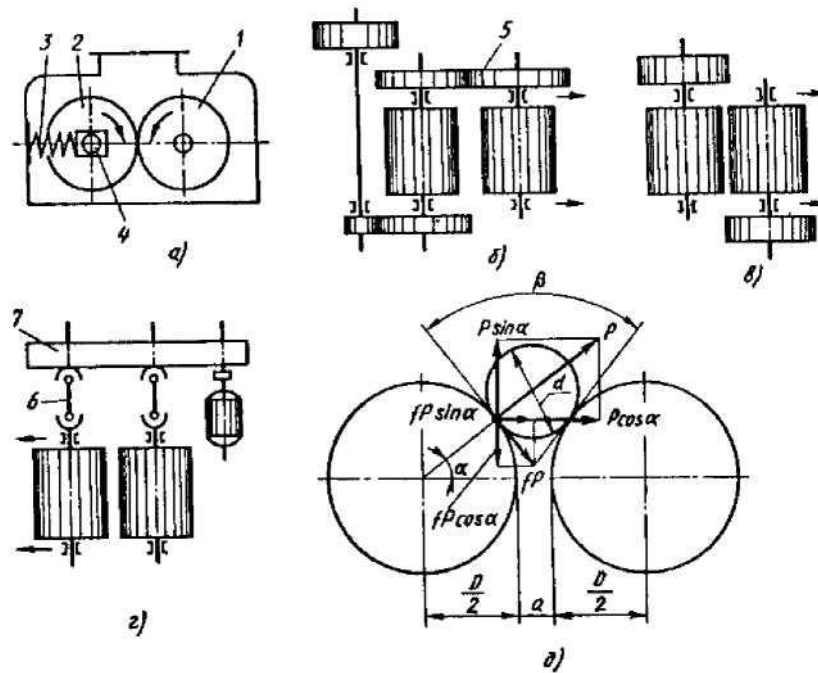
Схемы привода валковых дробилок: *a* - установка подвижного предохранительного вала; *б* - кинематическая схема дробилки с валками, связанными один с другим шестернями с удлиненными зубцами; *в* - с приводом валков от отдельных электродвигателей; *г* - через редуктор и карданные валы; *д* - расчетная схема валковой дробилки; 1 - ведущий валок; 2 - ведомый валок; 3 - пружина; 4 - опора с горизонтальным перемещением; 5 - шестерня с удлиненным зубом; 6 - карданный вал; 7 - редуктор
